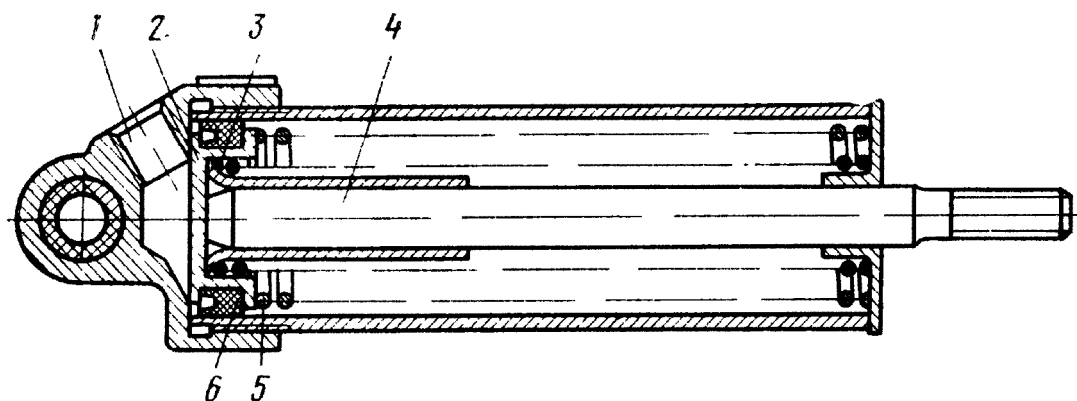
Пневматический цилиндр привода заслонки механизма вспомогательного тормоза.
